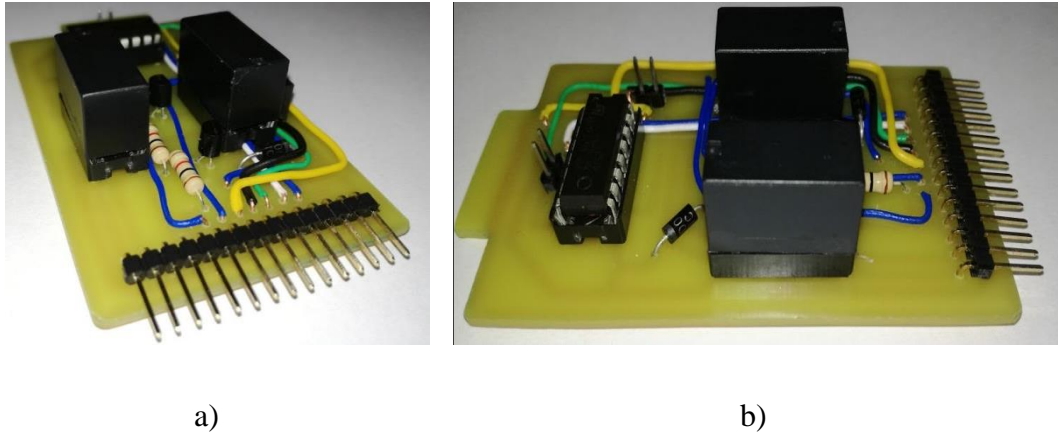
a) Vista frontal de la placa del prototipo b) Vista lateral de la placa del prototipo.
